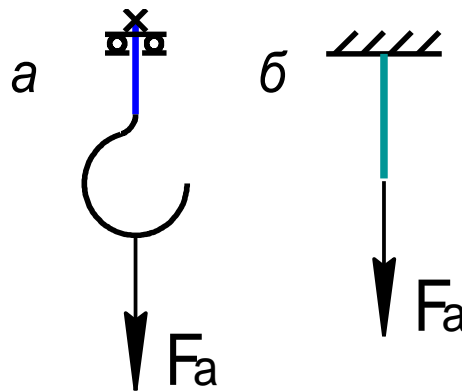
Вантажний гак і його розрахункова схема
